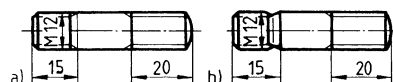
Einschraubende der Stiftschrauben, Gewindelänge (nutzbare)
